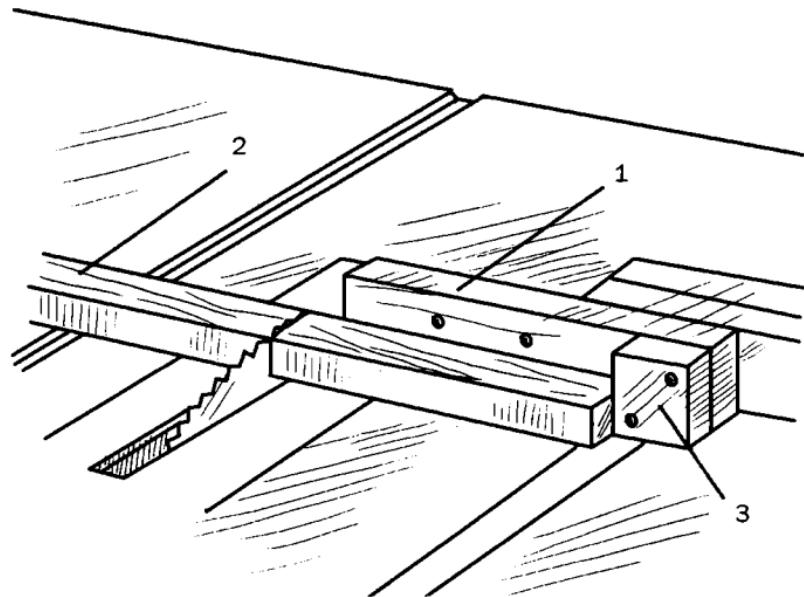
Использование шаблона с упором: 1 — направляющая линейка; 2 — заготовка; 3 — упор
